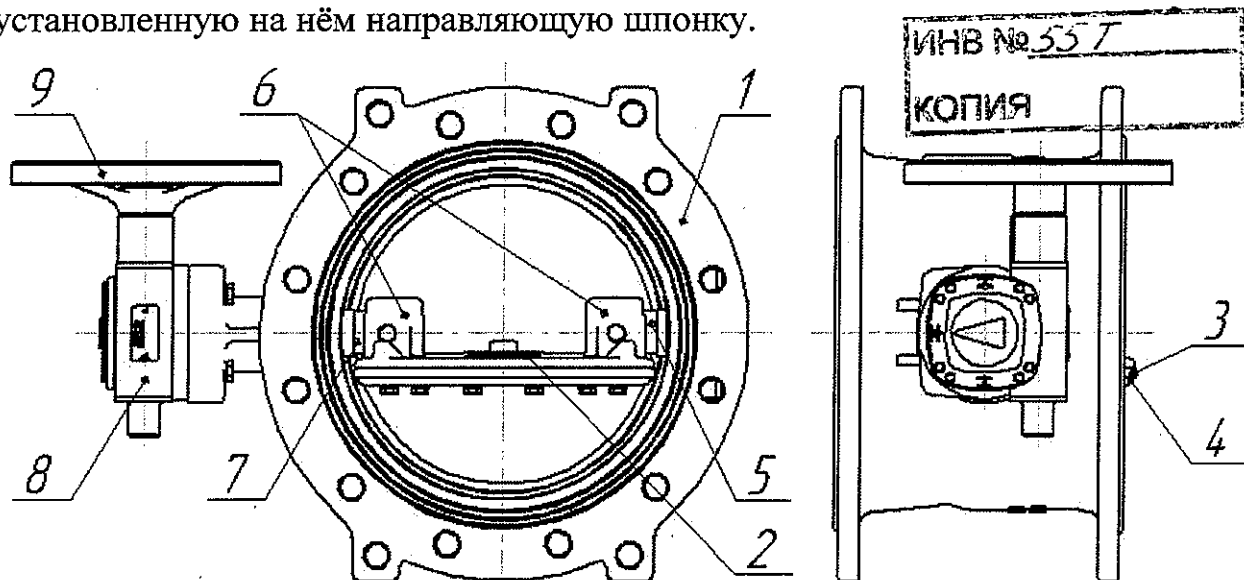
Устройство затвора с ручным приводом и маховиком
